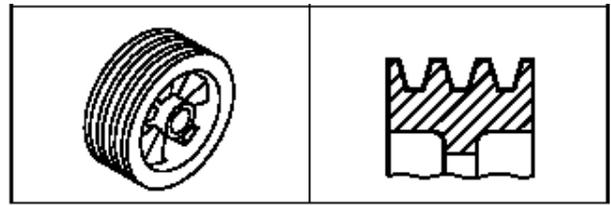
Polia com canal trapezoidal ou em “V”, múltipla.
